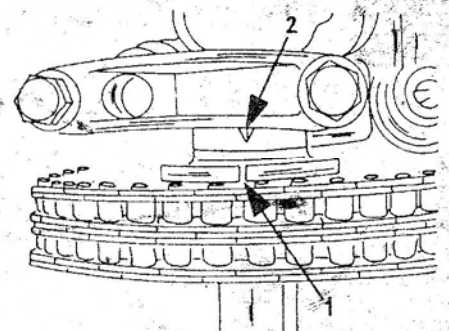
Положение верхней мертвой точки первого цилиндра. Насечка на фланце распределительного вала (1) должна совпадать с преливом на первой крышке подшипника распределительного вала (2).
